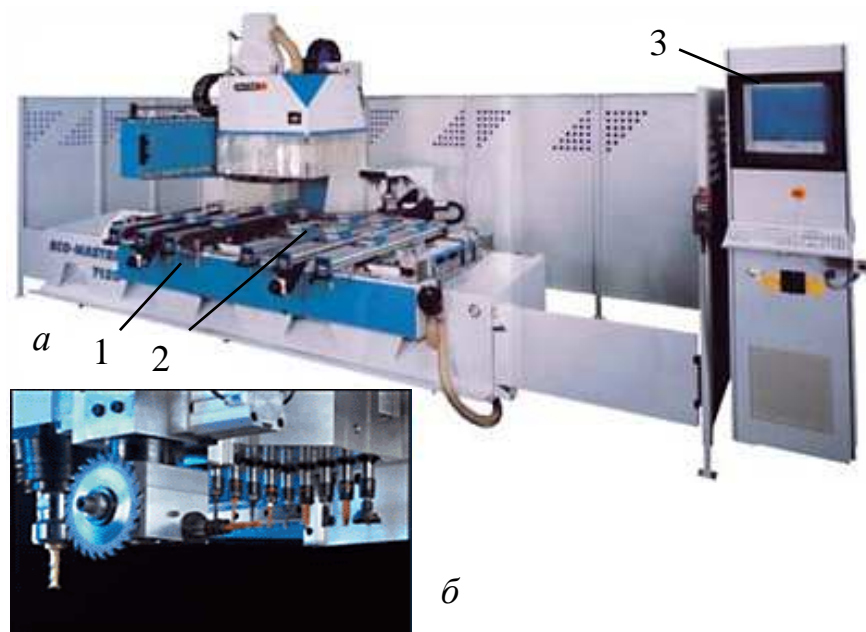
Универсальный обрабатывающий центр с ЧПУ Eco-Master: *а* – общий вид; *б* – суппорт с обрабатывающими шпинделями
